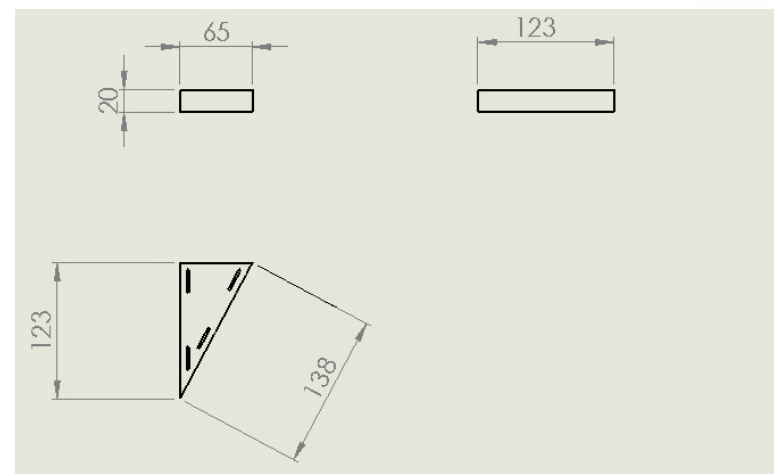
Desenho técnico da peça triangular de 123 x 65 x 20 mm
